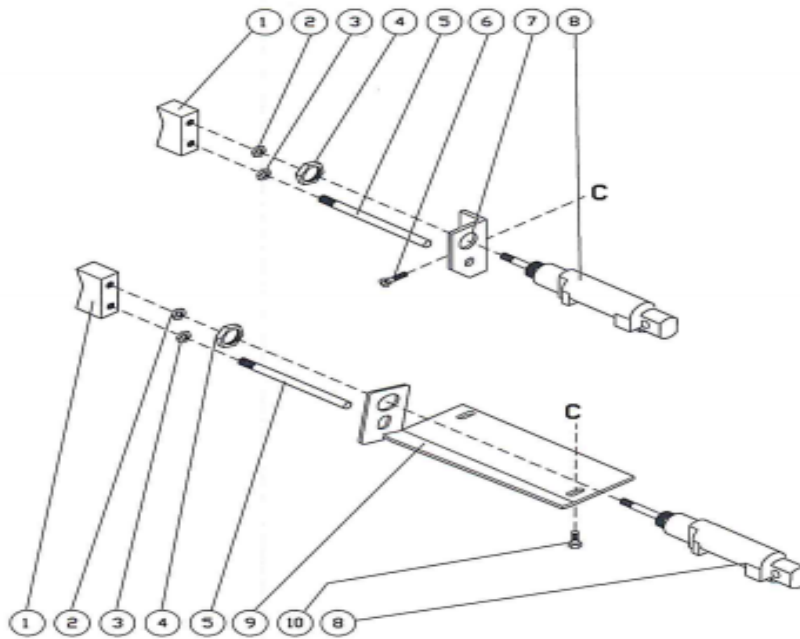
Imagen de Despiece del Equipo: Dispositivo de Corte Cadeneta.
